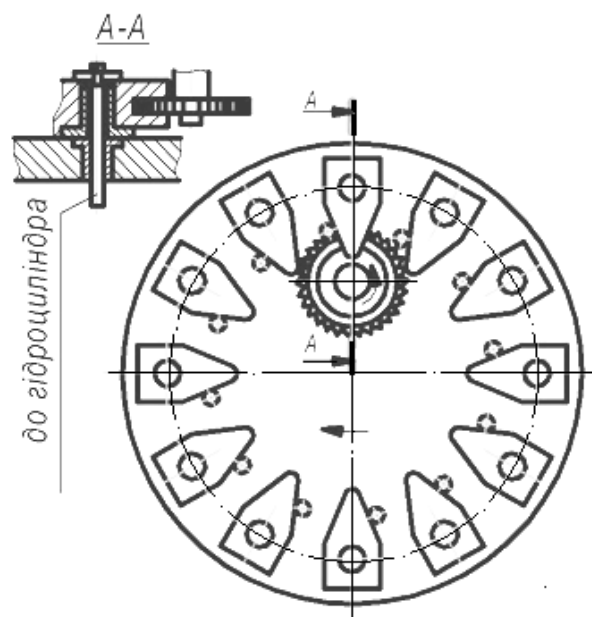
Схема неперервного фрезерування паза у важелів на горизонтально-фрезерному верстаті з обертовим столом
